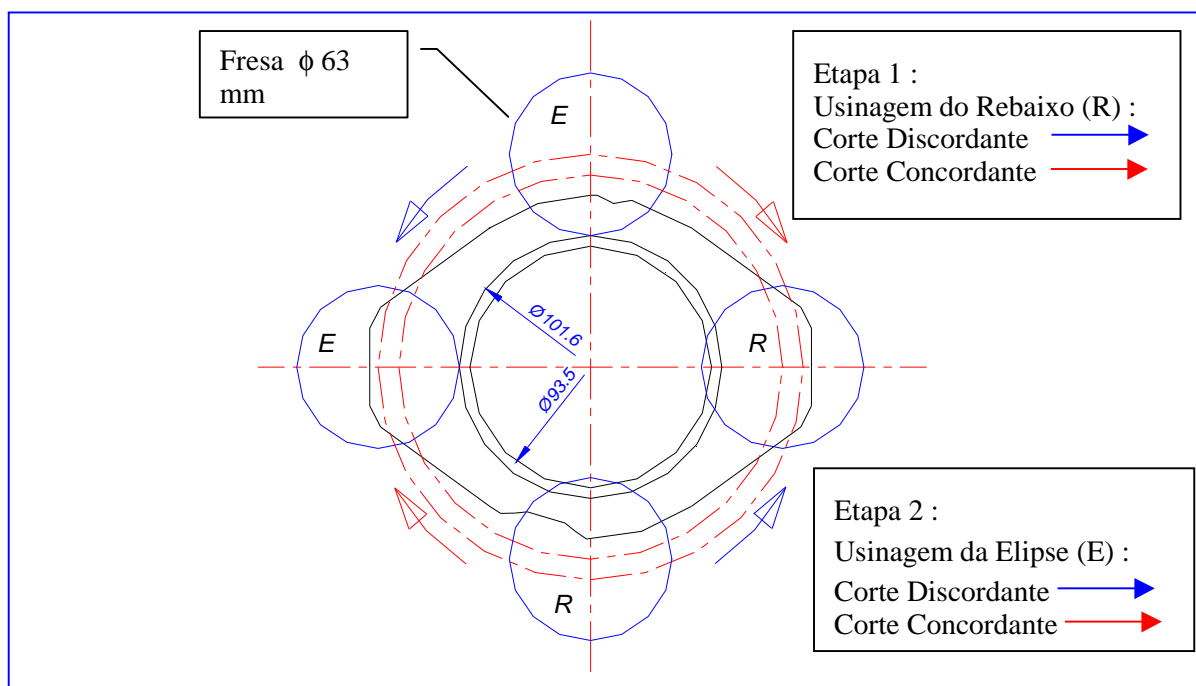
Usinagem da Peça 1 nos sentidos concordante e discordante
